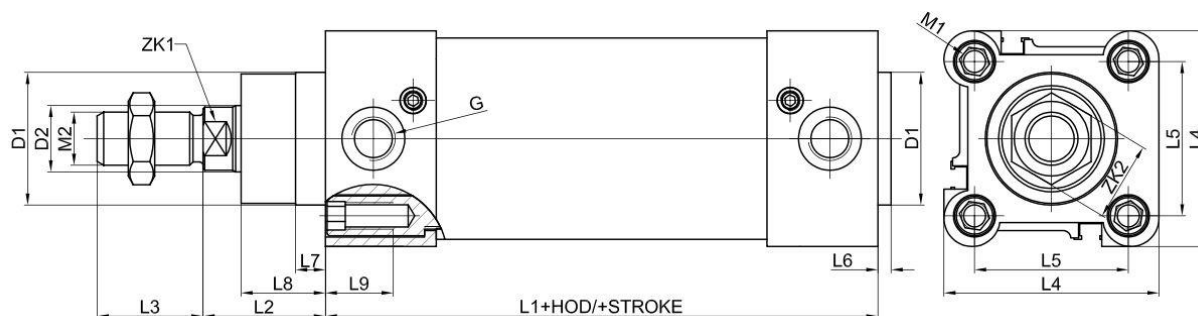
Pneumatski cilindar - UNI AIR PNCU 63 [27]
